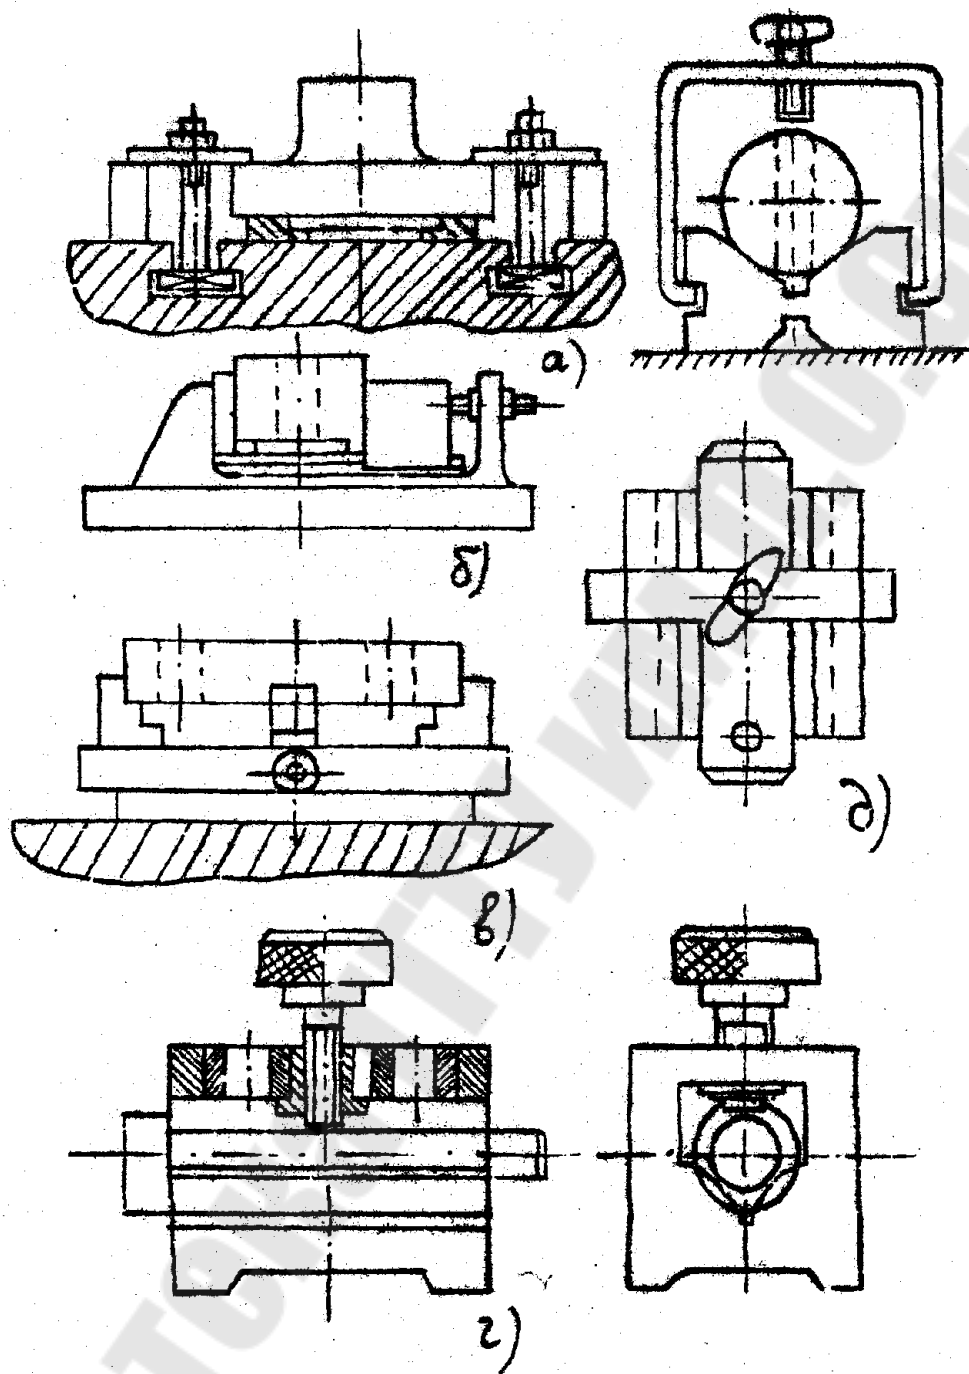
Приспособление для закрепления заготовок на сверлильных станках
